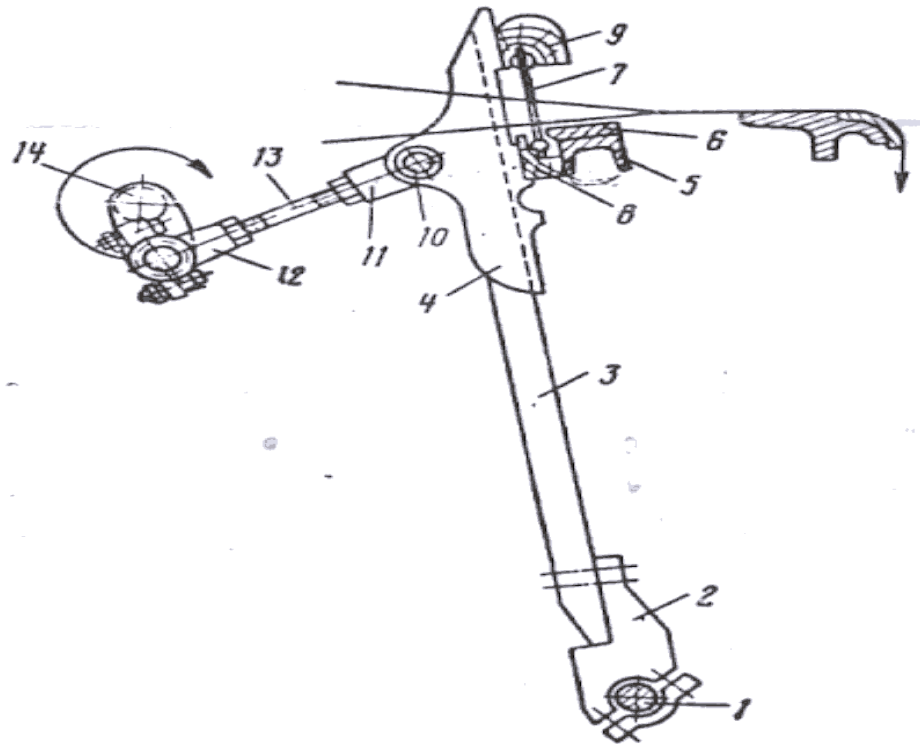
схема батанного механизма станка АТ – 100 – 5М
